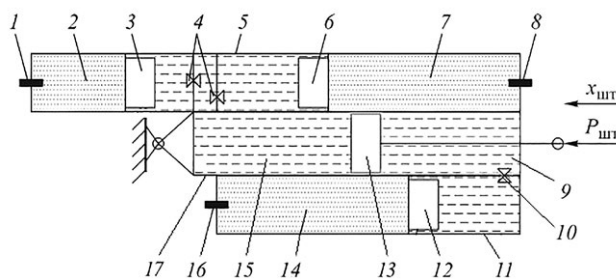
Конструктивная схема ДУ ГПР с ПД: 1, 8, 16 – зарядный клапан; 2, 7, 14 – пневматическая полость; 3, 6, 12 – поршень-разделитель; 4, 10 – дросселирующая система; 5, 11 – пневмоцилиндры; 9 – штоковая полость гидроцилиндра; 13 – поршень со штоком; 15 – поршневая полость гидроцилиндра; 17 – гидроцилиндр; $X_{шт}$ – направление перемещения штока при прямом ходе подвески; $P_{шт}$ – направление действия силы.
